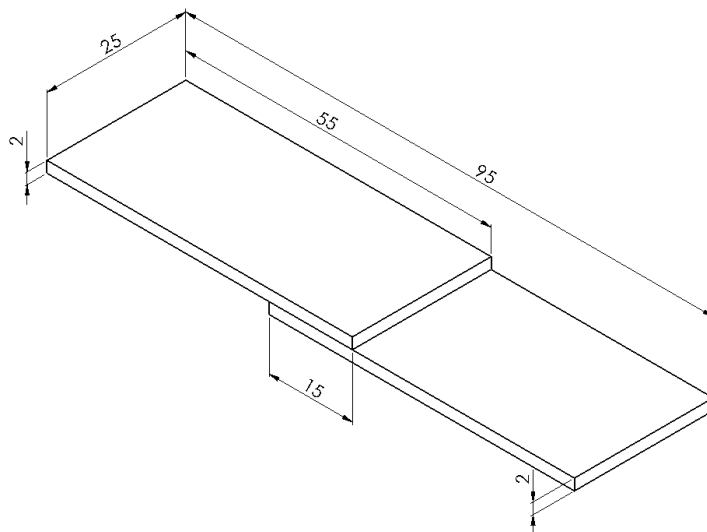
Dimensões da junta adesiva de cada provete (dimensões em mm)
